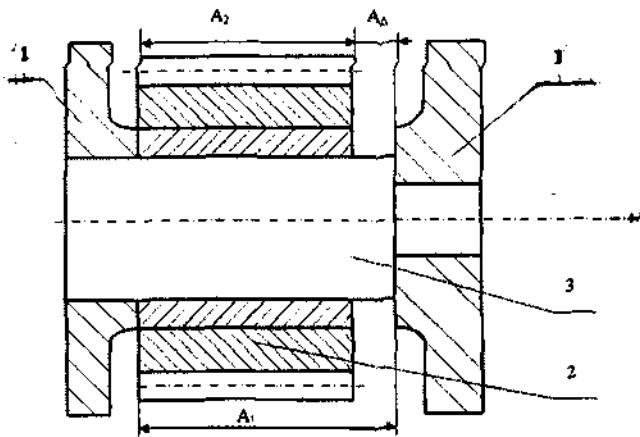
Сборочный чертеж: 1 – стаки; 2 – зубчатое колесо; 3 – ось
